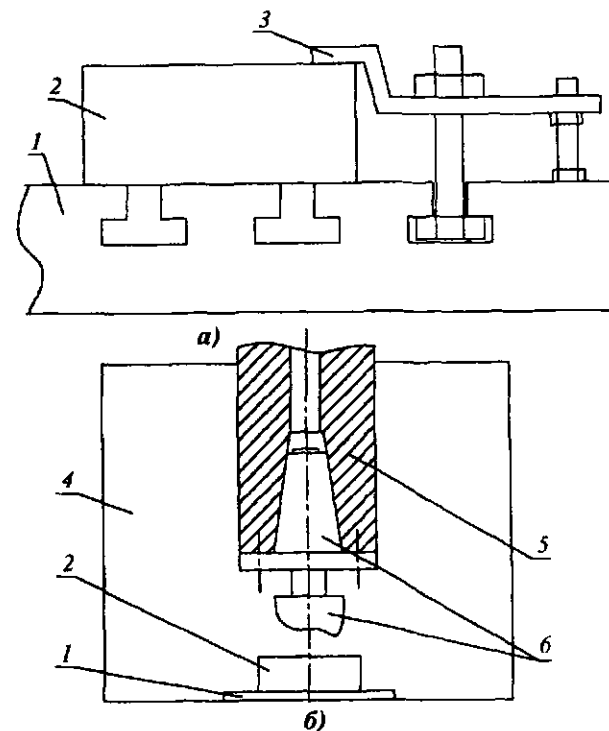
Крепление заготовки (а), инструмента (б) при прошивании на ЭХО: 1 – стол; 2 – заготовка; 3 – прихват; 4 – камера; 5 – планшайба; 6 – инструмент
